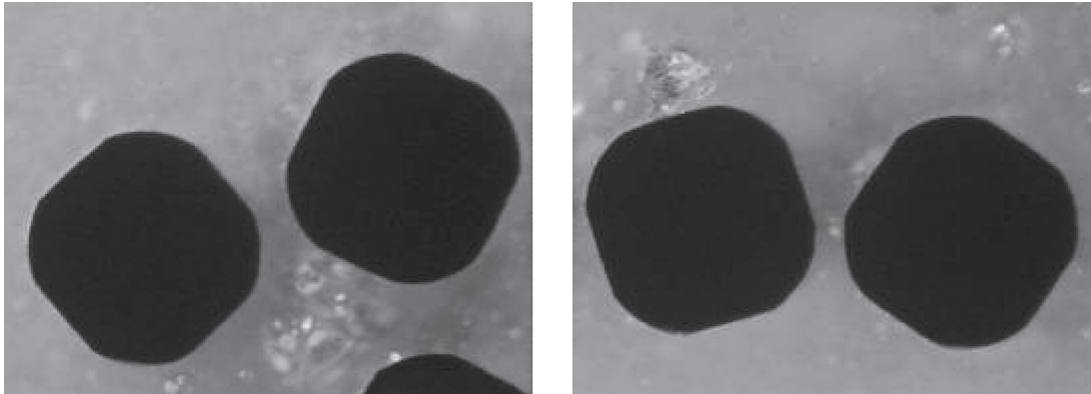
Поперечное сечение квадратной проволоки размером 0,54×0,54 мм, изготовленной с проволочной заготовки диаметром 0,57 мм. ×53
